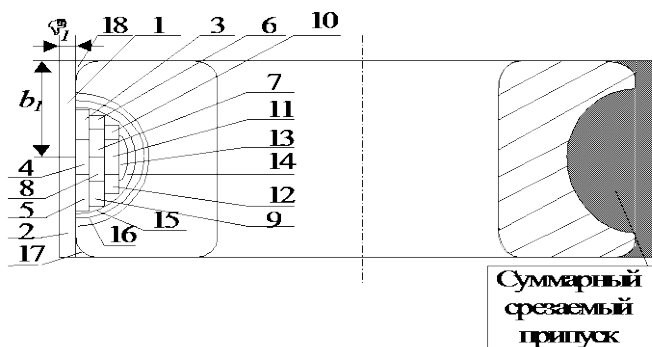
Схема снятия припуска при обработке внутреннего кольца подшипника на станке КА-350
